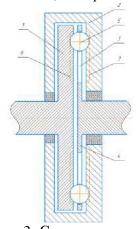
Схема торцевой цилиндрической передачи с ПТК
